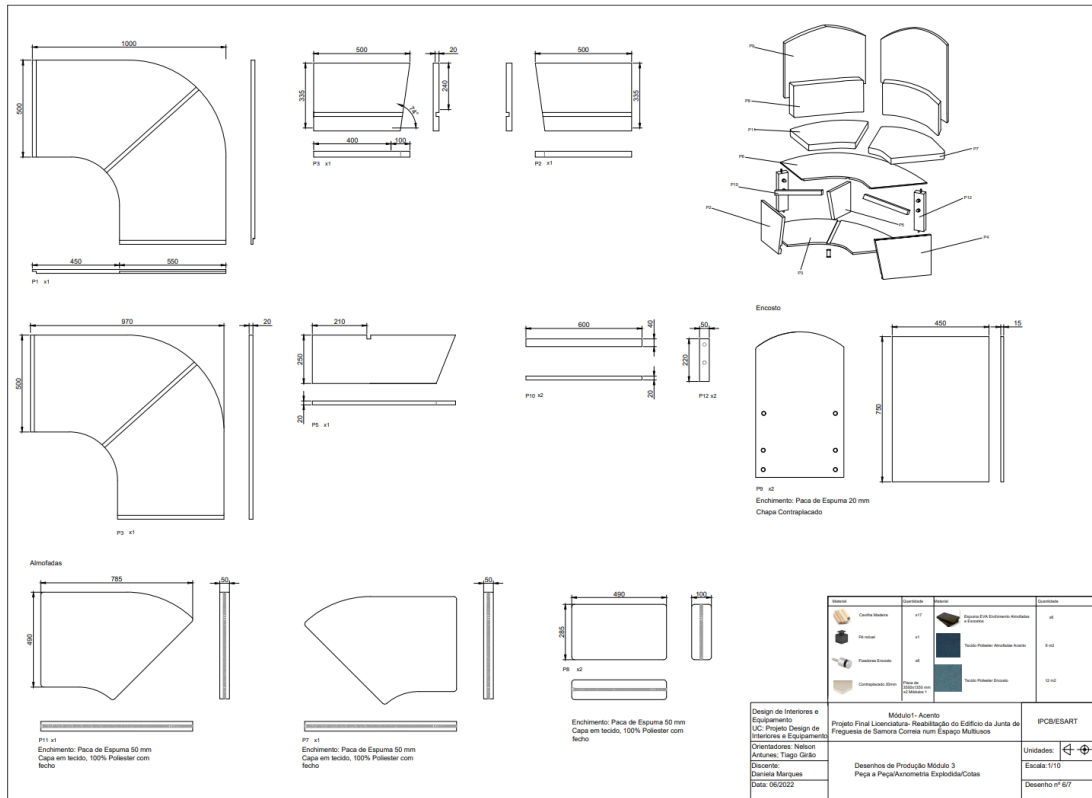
Figura 102-Desenho Técnico Produção Módulo 3
